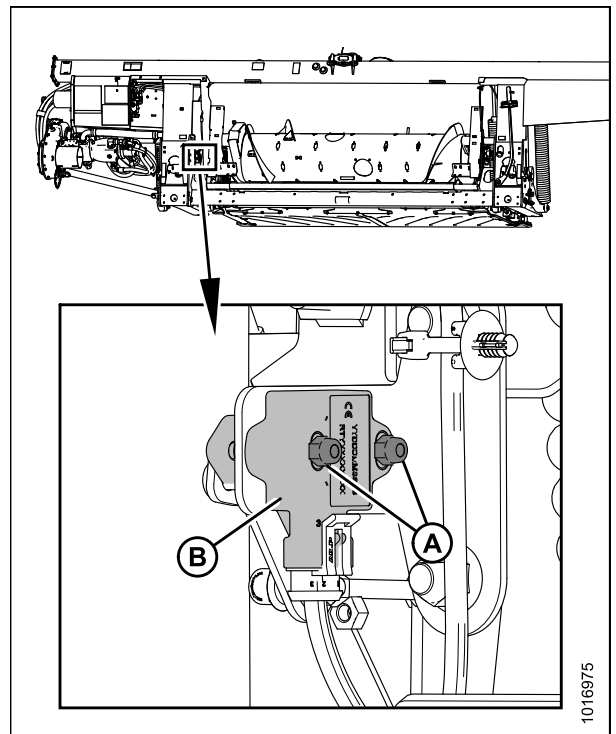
Kit opcional de 2 sensores: sensor izquierdo
